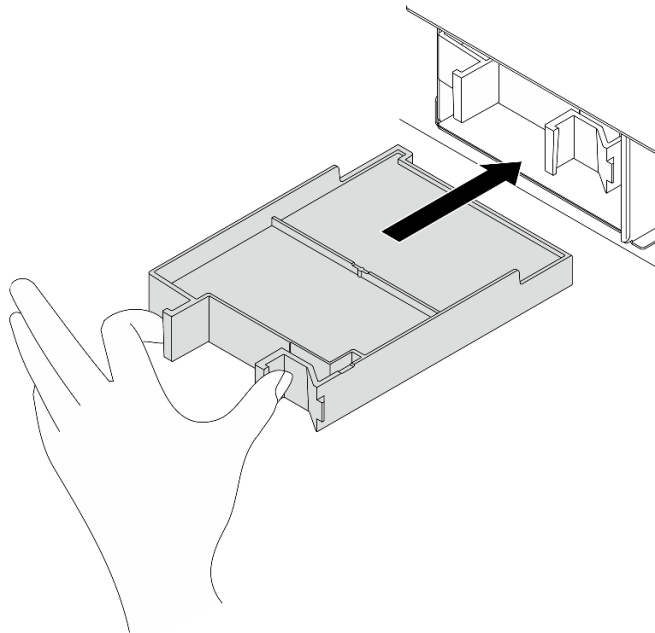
Installieren einer CMM-Abdeckblende für Laufwerkposition
